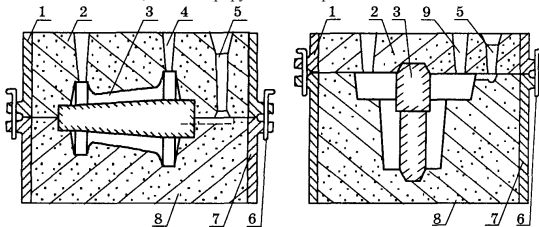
Эскизы литейных форм в сборке: 1 — верхняя опока;
